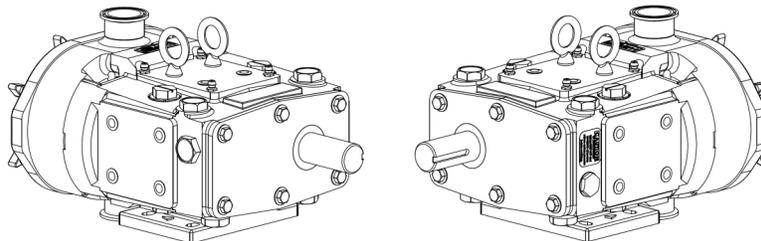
Montaje de flecha motriz lateral derecha e izquierda
